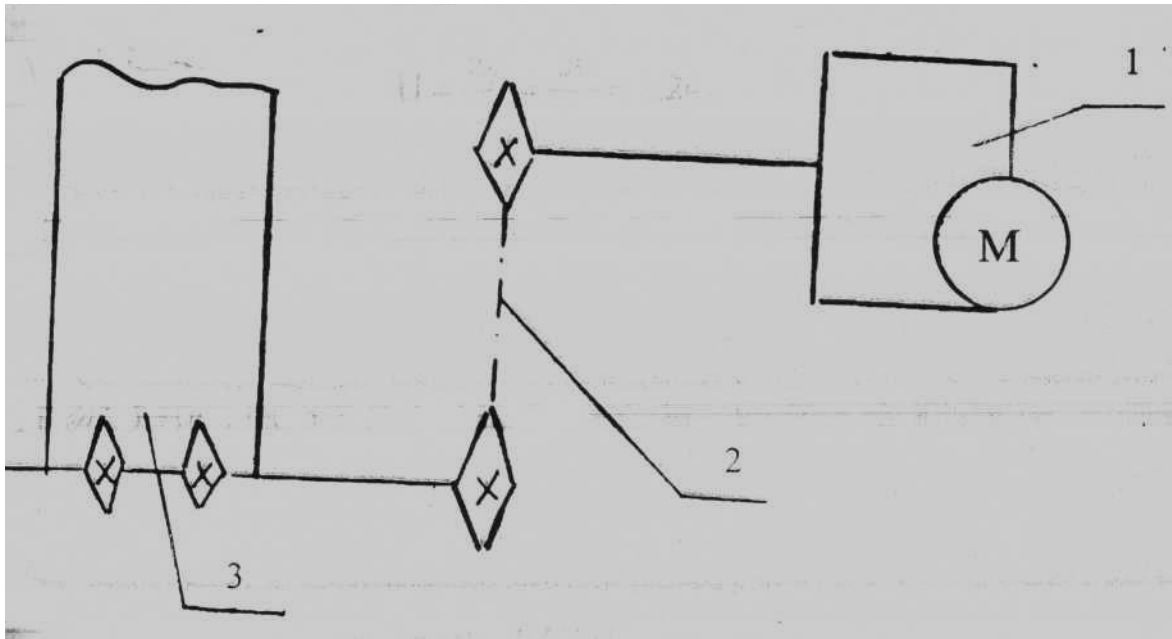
Схема привоу: 1 – мотор-редуктор; 2 – ланцюгова передача; 3 – привідний вал з опорами
